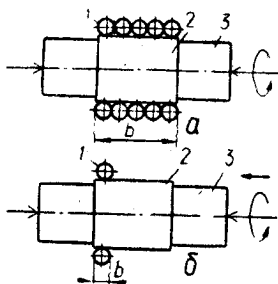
Схема індукційного наплавлювання зовнішніх циліндричних поверхонь:
